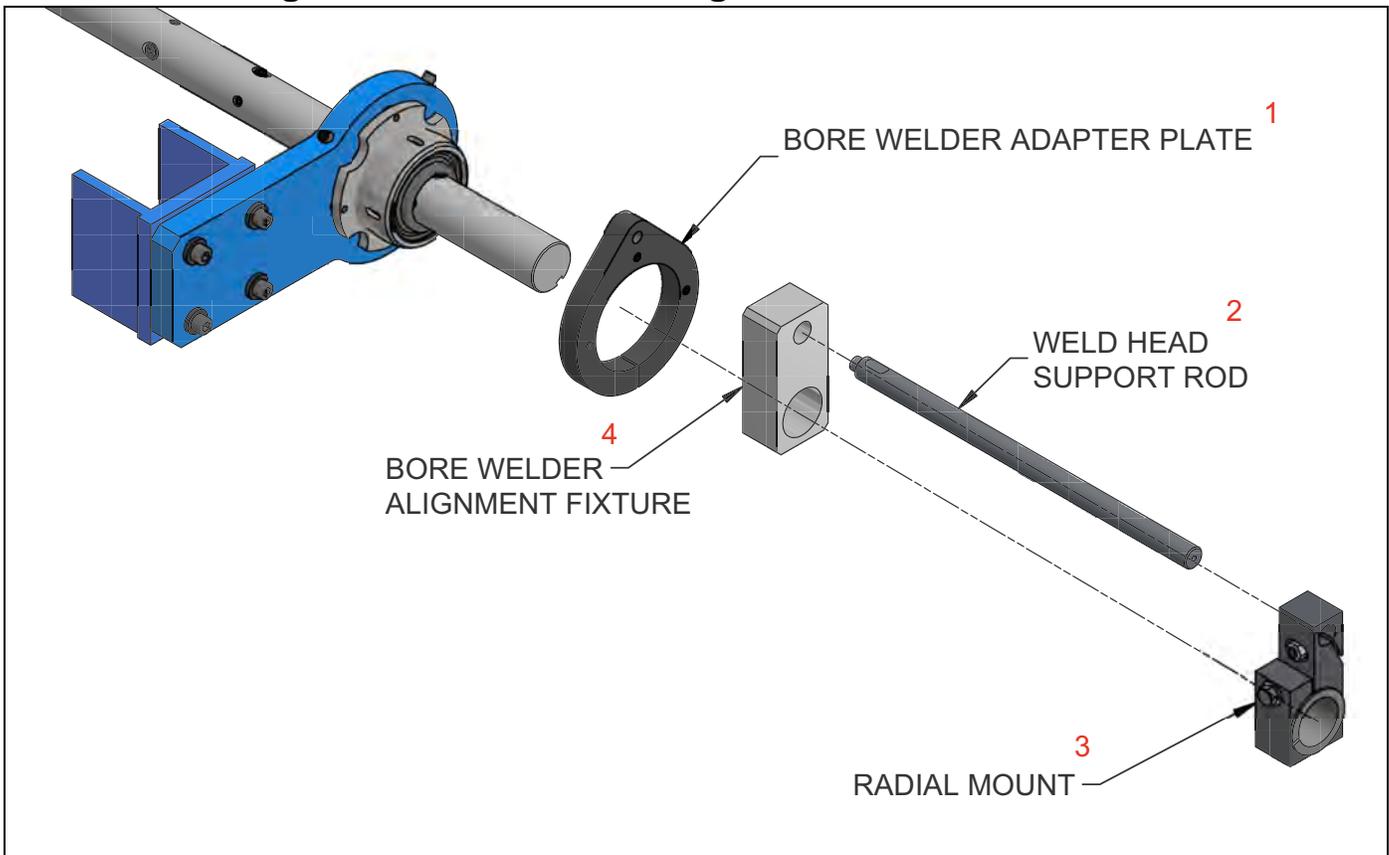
DÉTAILS DE L'INSTALLATION DU KIT D'ADAPTATEUR DE LA BARRE D'ALÉSAGE
